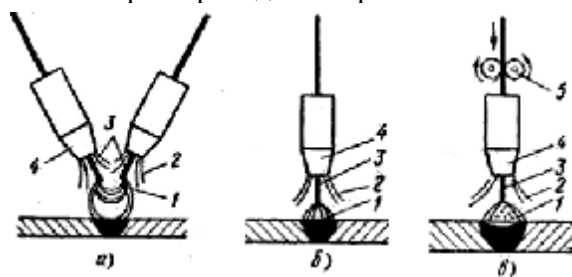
Схема газозлектрического способа дуговой сварки: а — дугой косвенного действия; б — дугой прямого действия неплавящимся электродом; в — дугой прямого действия плавящимся электродом; 1 — электрическая дуга; 2 — защитный газ; 3 — электрод; 4 - газовое сопло; 5 — подающие ролики
